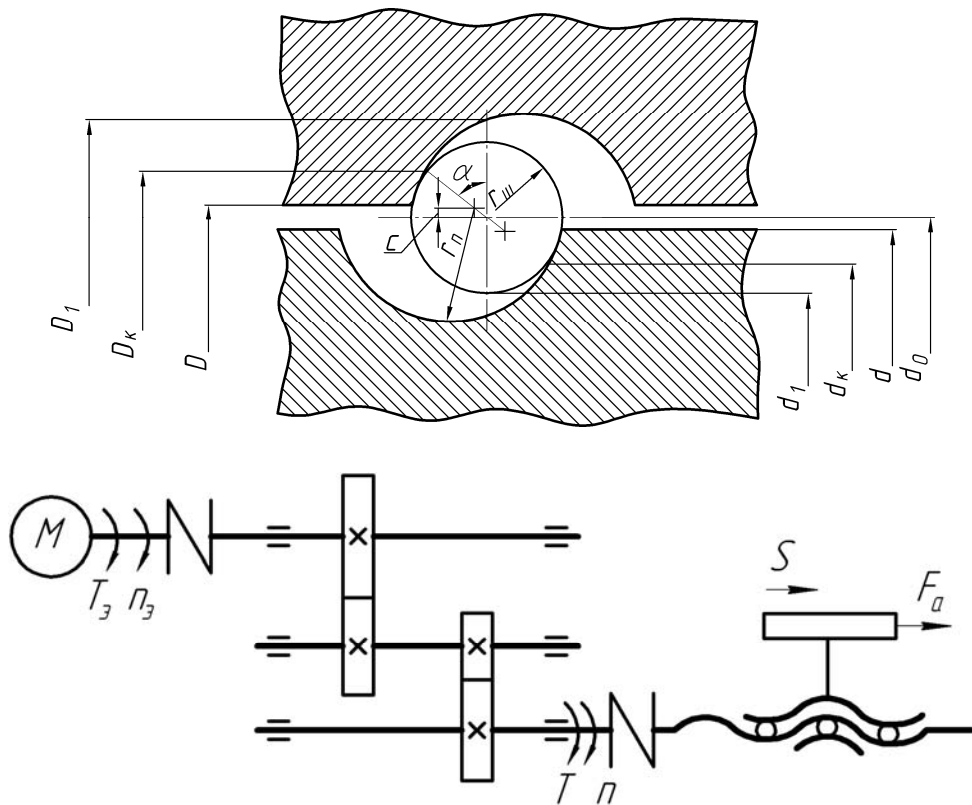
Основные размеры и кинематическая схема привода
